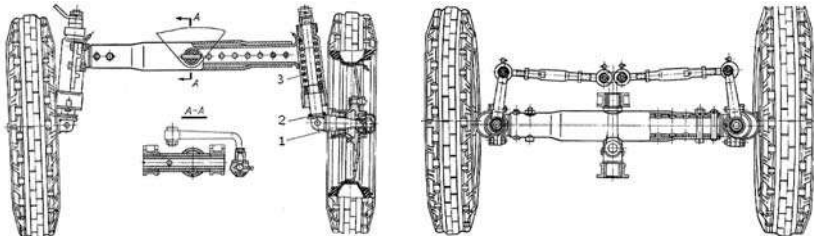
Передня вісь з підресореними напрямними колесами:
